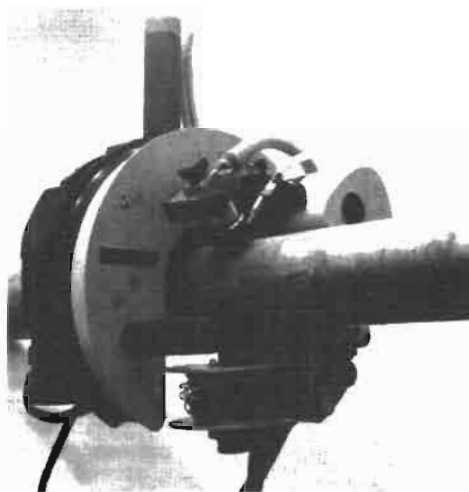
Головка ОКА-1 для орбитальной сварки корневых швов труб диаметром 76...133 мм неплавящимся электродом без присадки
